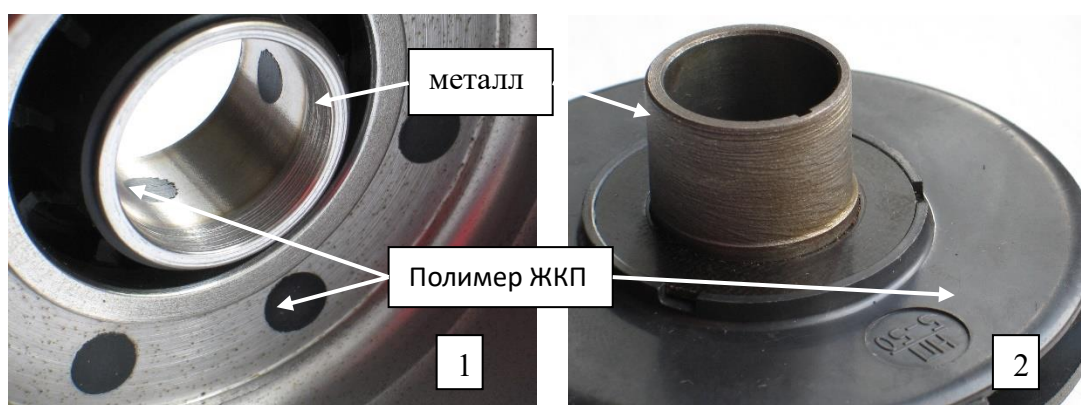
Общий вид деталей ступени из полимера ЖКП: 1-направляющий аппарат; 2-рабочее колесо
